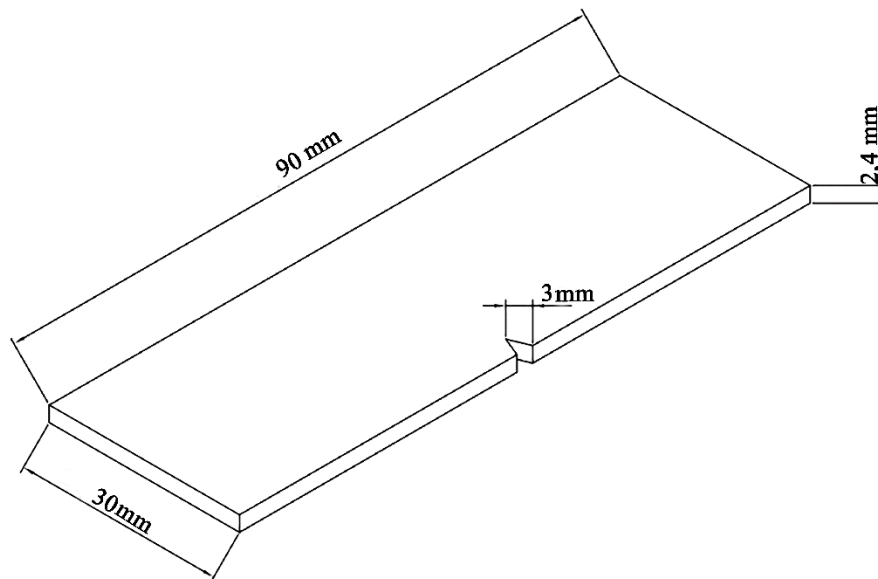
Géométrie et dimensions en mm des éprouvettes SENT (en mm).
